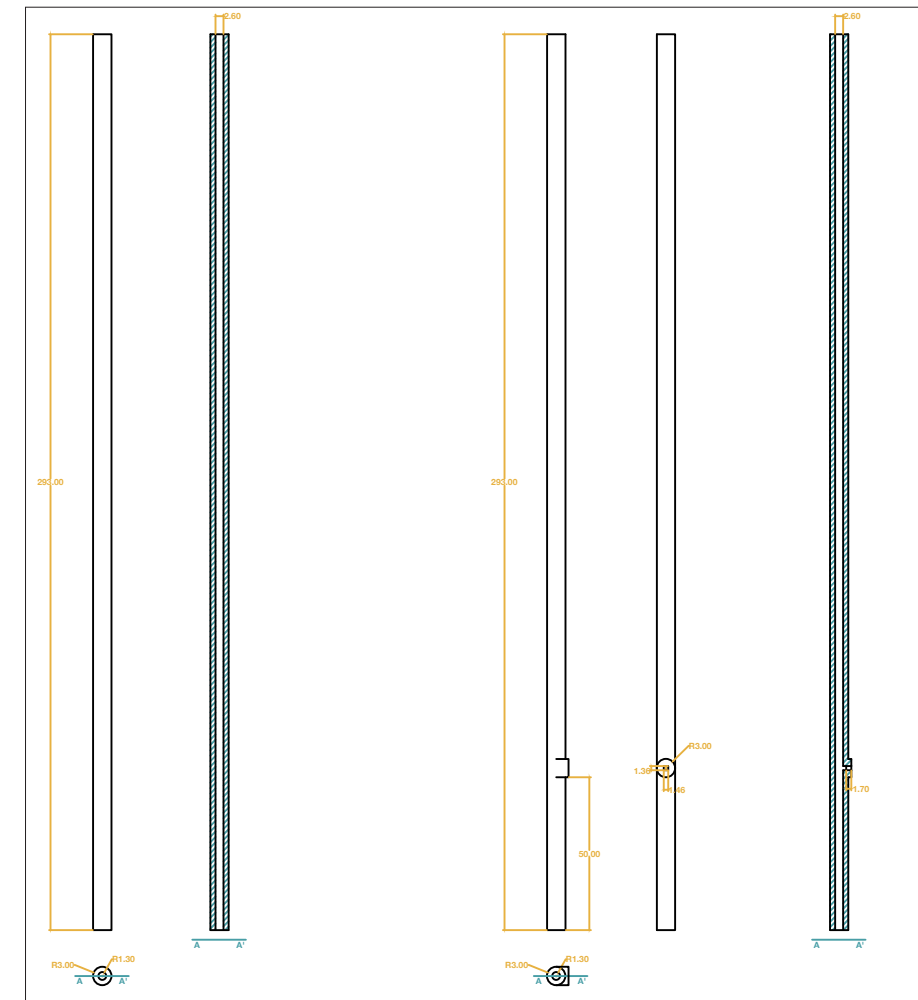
Planta, alzado, perfil y sección de la Columna 293 A y de la Columna 293 B.
